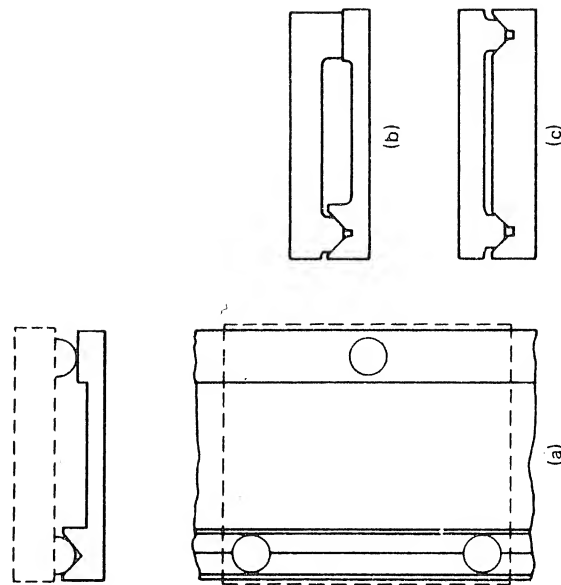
Diseños de guías. (a) Diseño cinemático; (b) diseño sobre-determinado; (c) diseño sobre-determinado.
